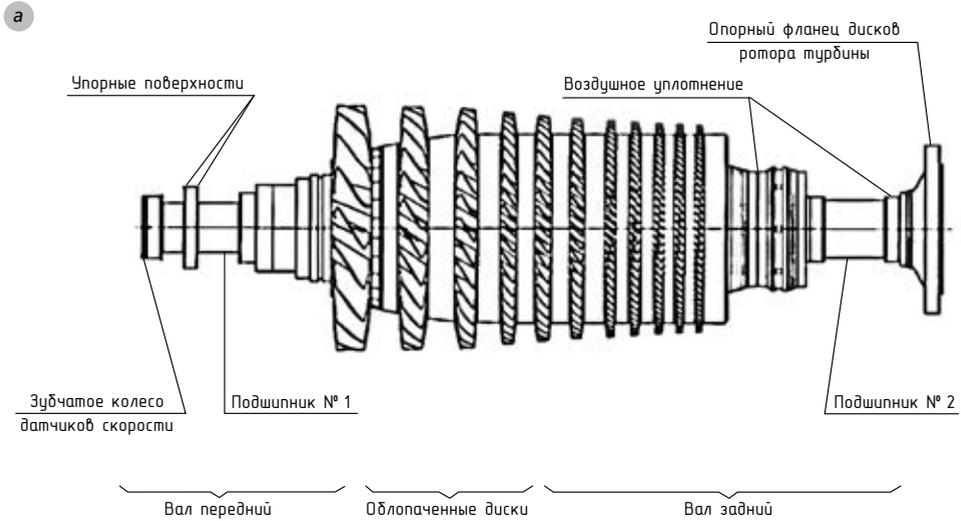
Ротор компрессора: а) схема ротора компрессора;
